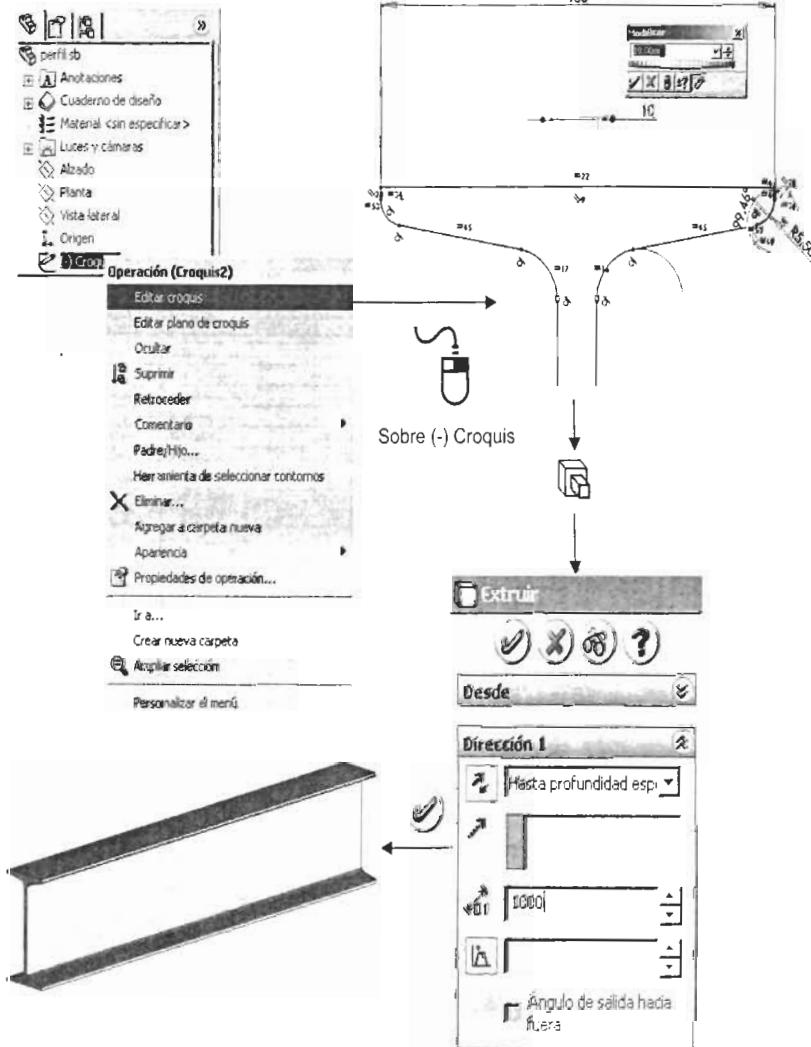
Modificación y Extrusión del perfil Viga SB.
